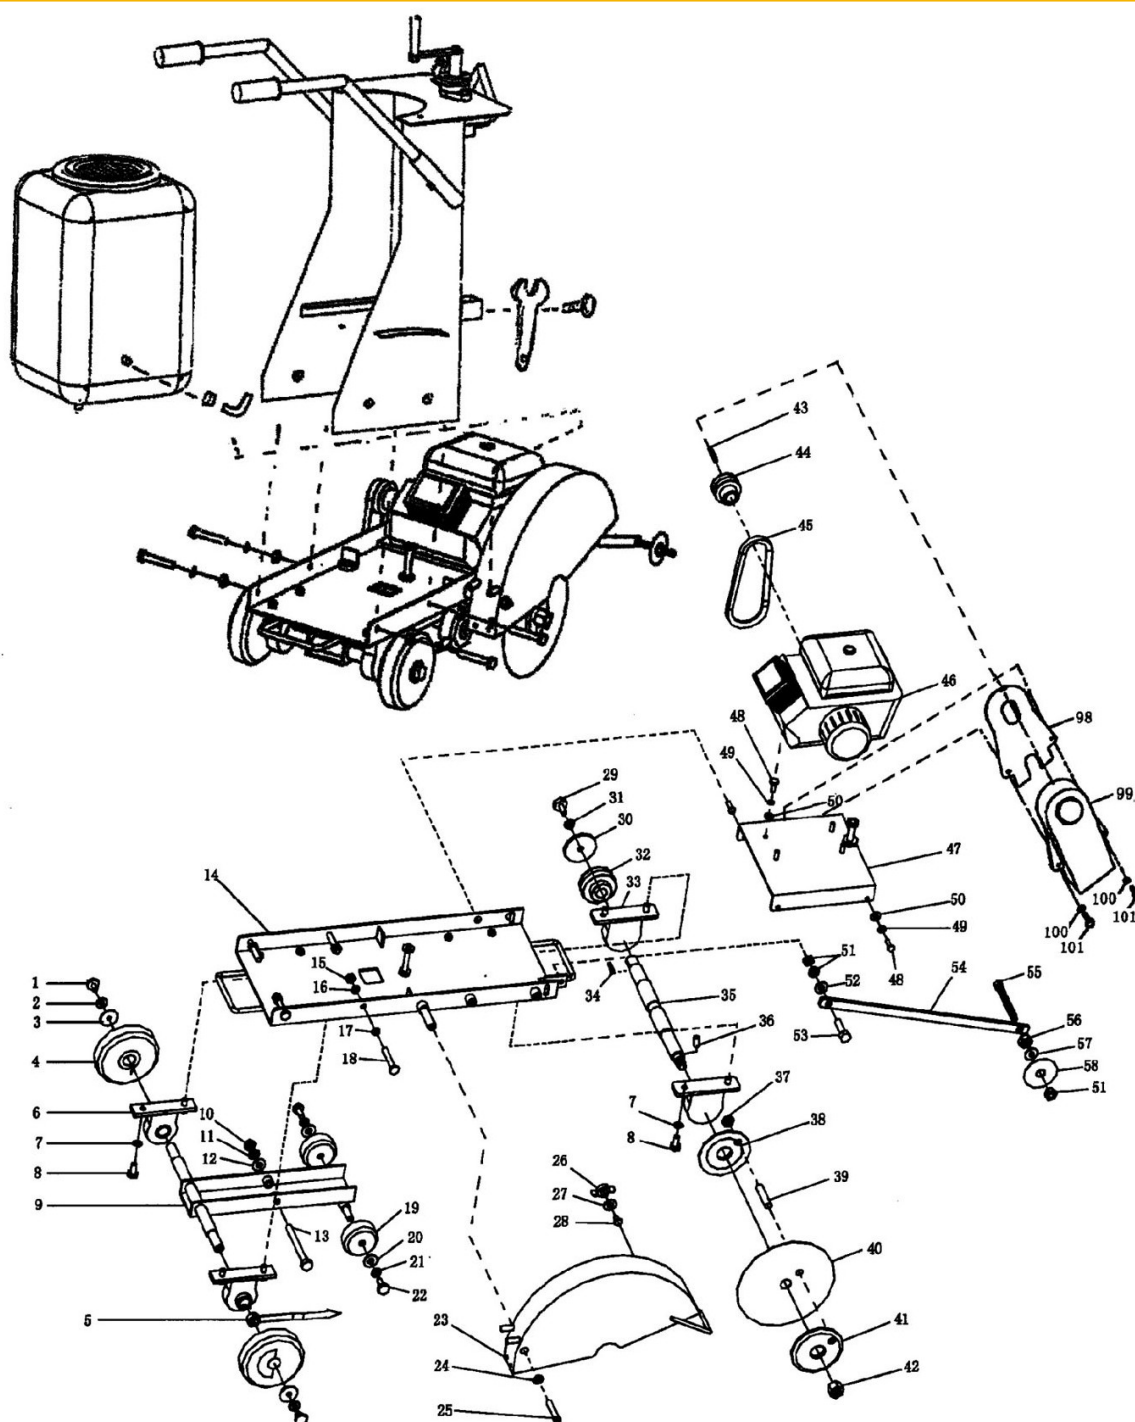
Vista explodida: chasis, transmissão e grupo de corte
